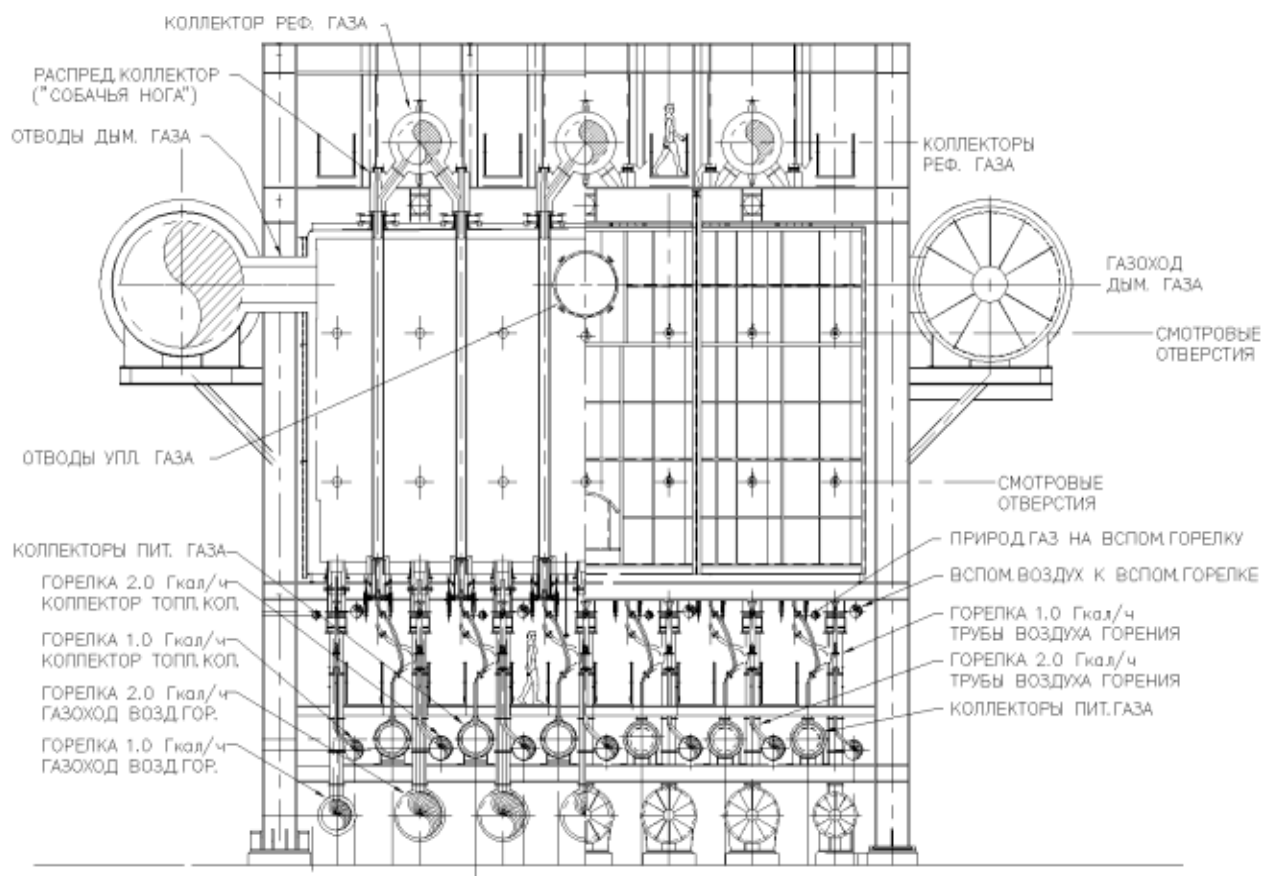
Реформер установки MIDREX. Вид с торца
